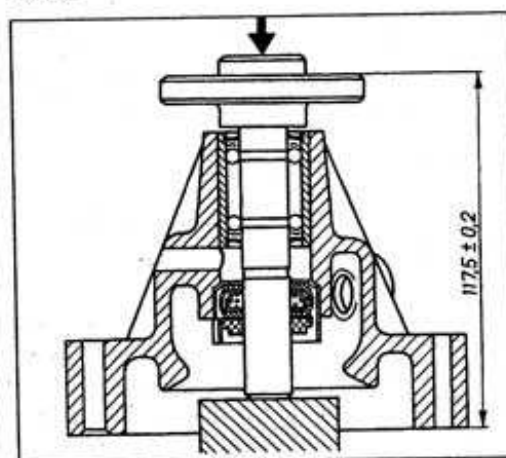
Напрессовка ступицы шкива насоса на вал
